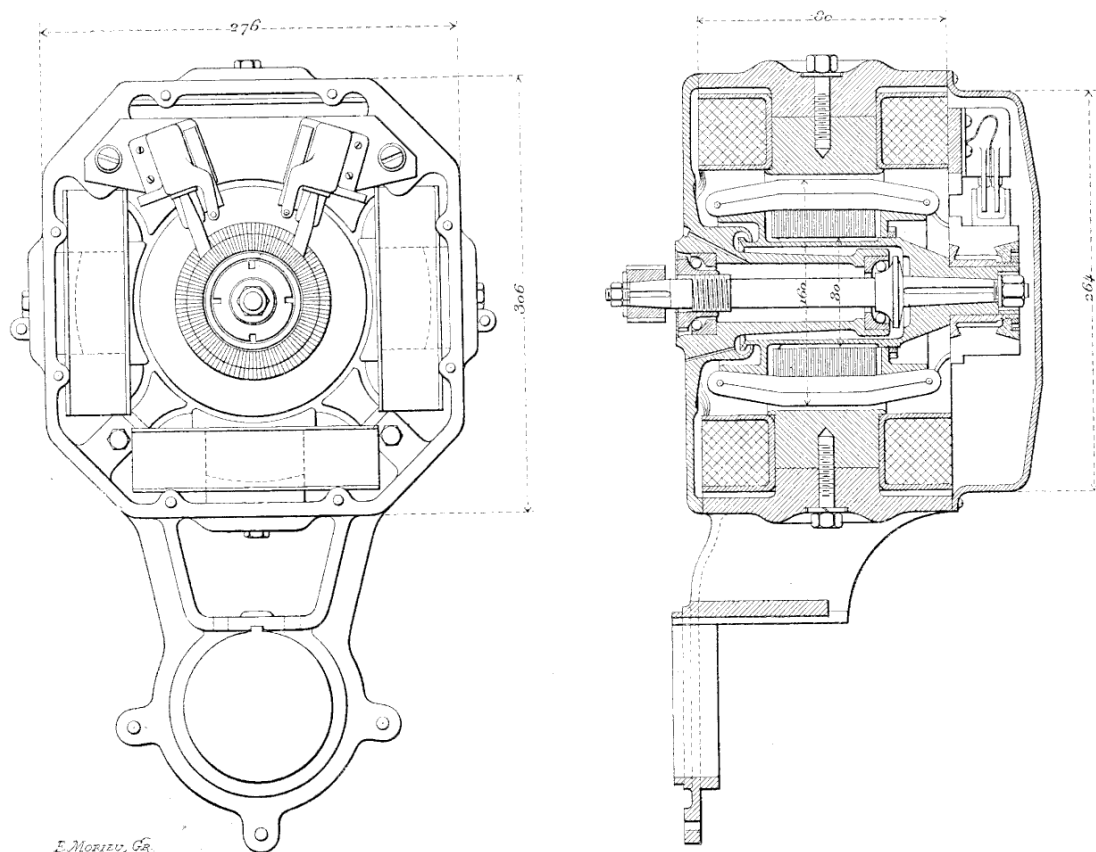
Vue en élévation et vue en coupe verticale du moteur Krieger.
